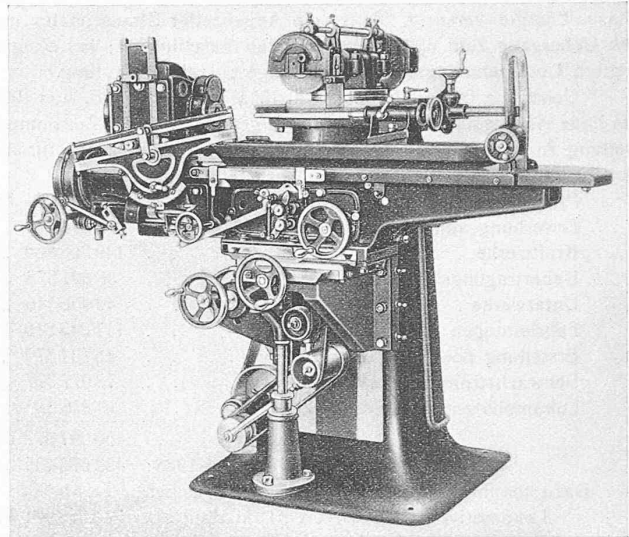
Werkzeug-Schleifautomat der Grossenhainer Webstuhl- und Maschinenfabrik A.-G., Grossenhain.
